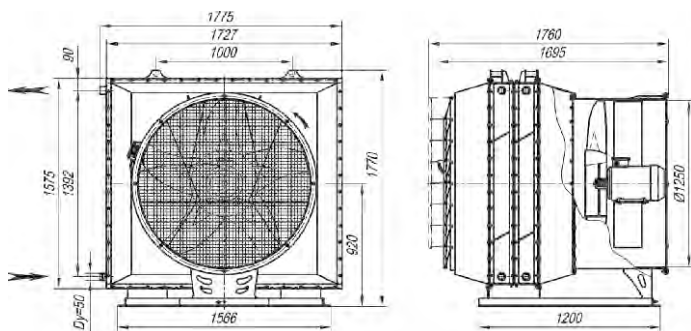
Габаритные и присоединительные размеры агрегата А02-50 на базе двух водяных калориферов КСк 3-12-02 ХЛЗ.
